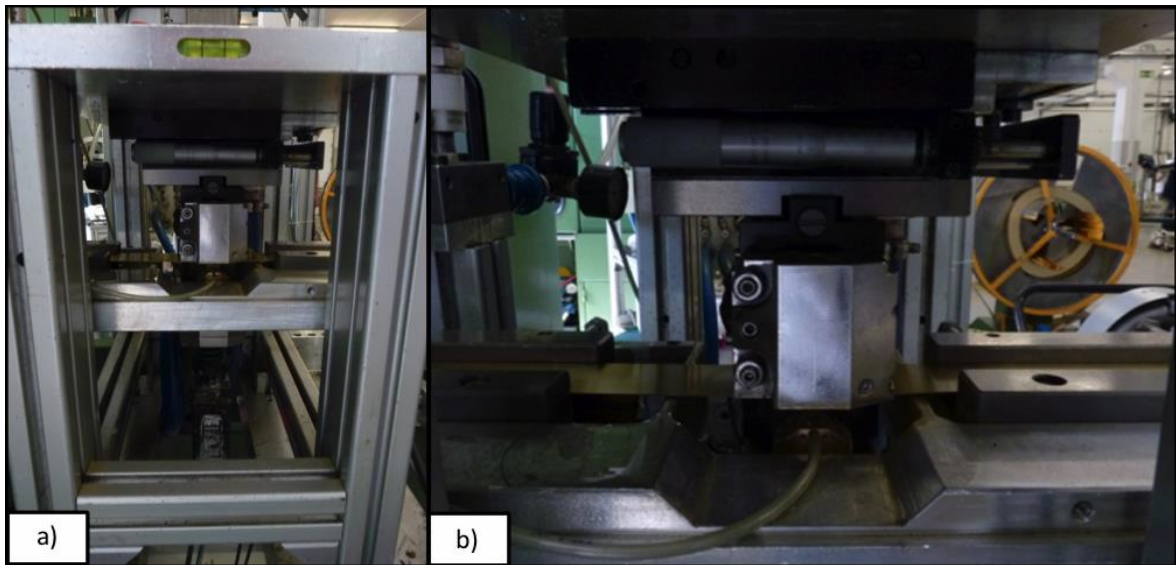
a) sistema de soldadura b) sistema de afinação da soldadura
